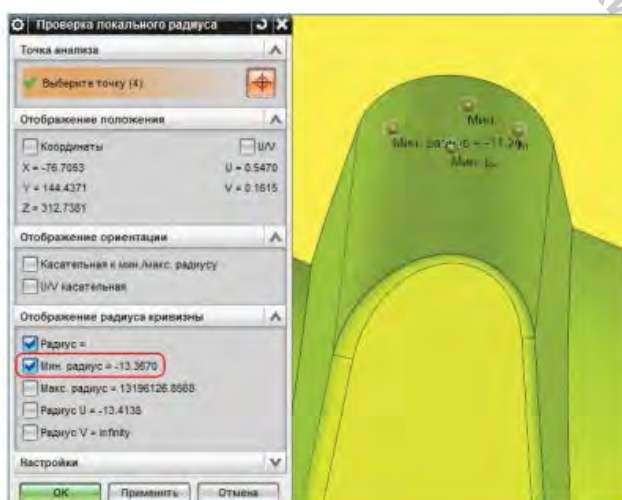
Значения локального радиуса элемента формообразующей полости детали
